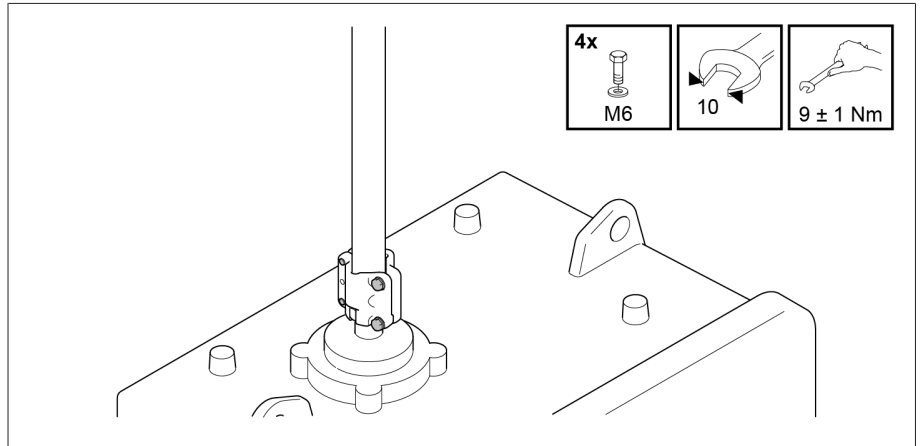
Fixer le tube carré sur le mécanisme d'entraînement
